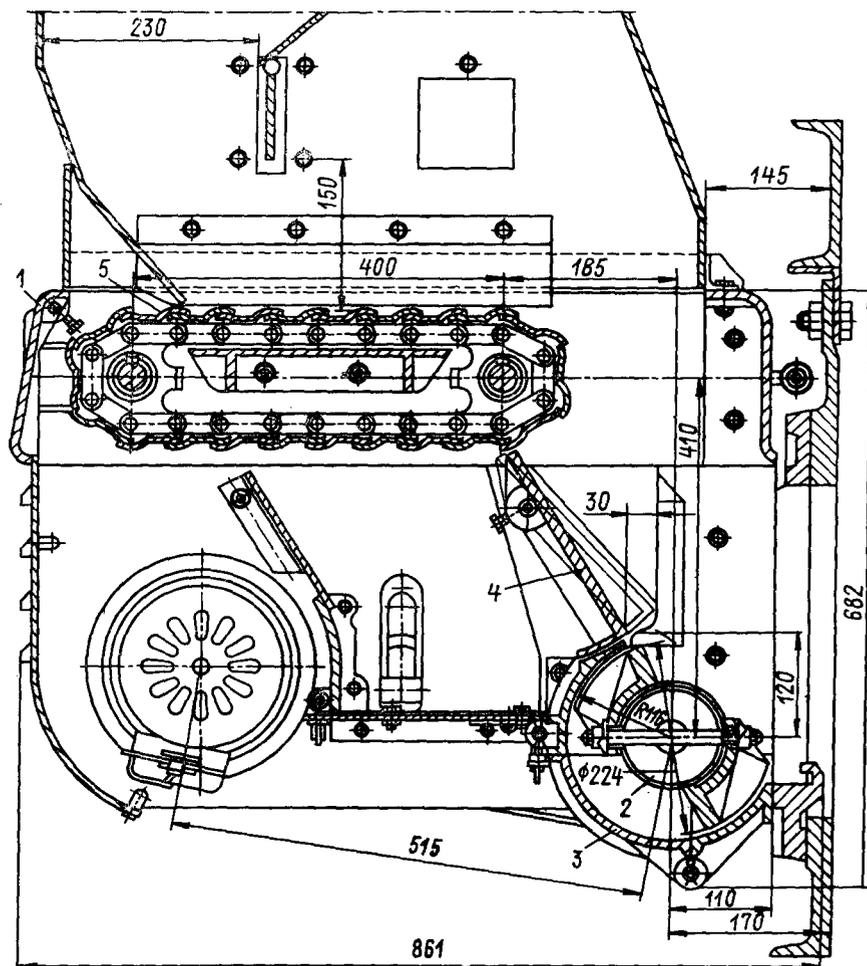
Пневмомеханический забрасыватель с пластинчатым питателем:
